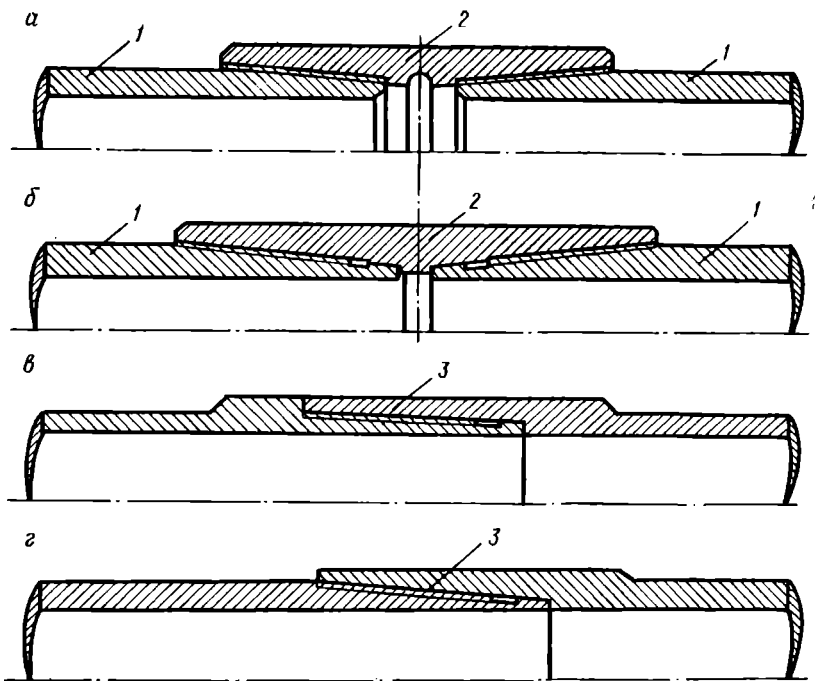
А. Новые конструкции резьбовых соединений обсадных труб:
